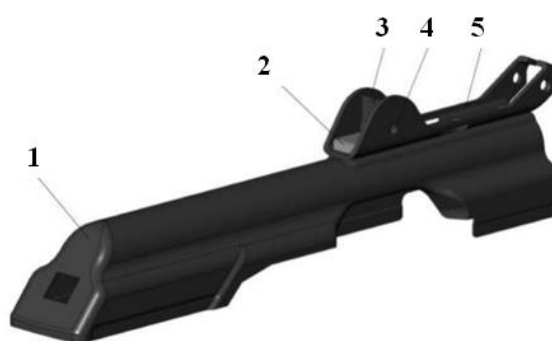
Крышка ствольной коробки пистолета-пулемета «Витязь»: 1 – крышка; 2 – пружина целика; 3 – целик; 4 – ось целика; 5 – корпус прицела
